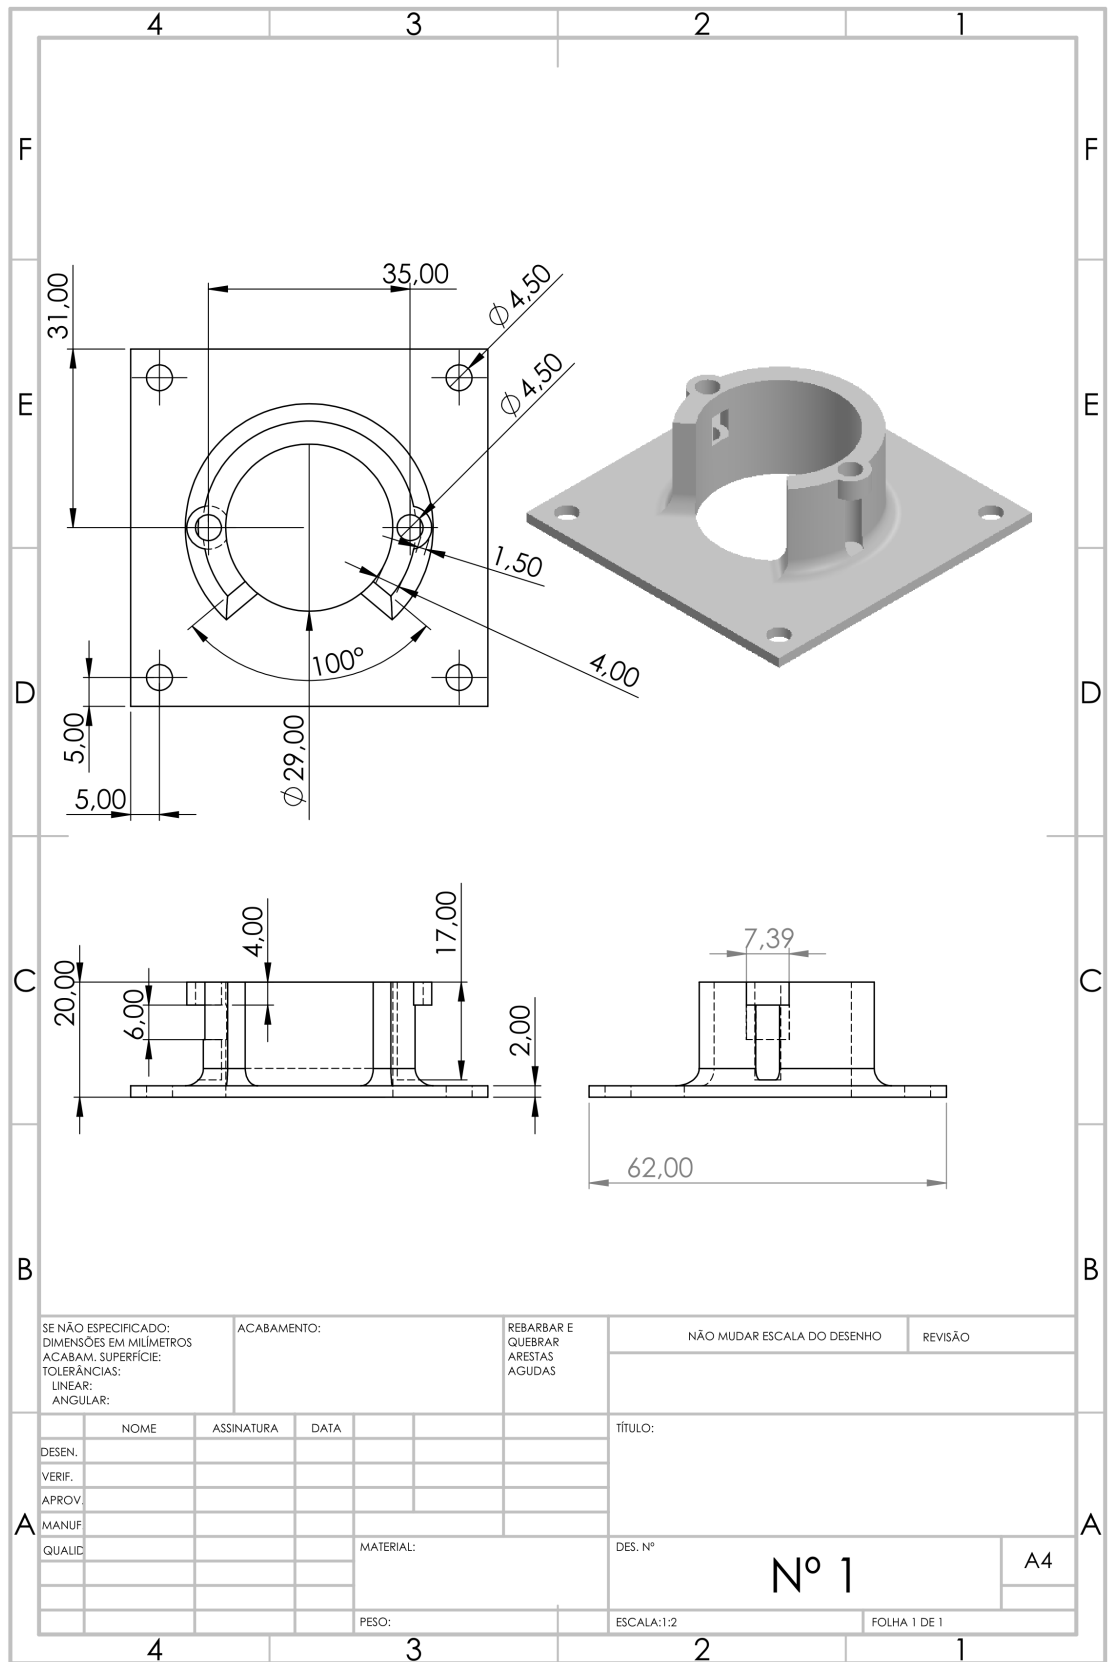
Desenho Técnico da Base do Motor de Passo
